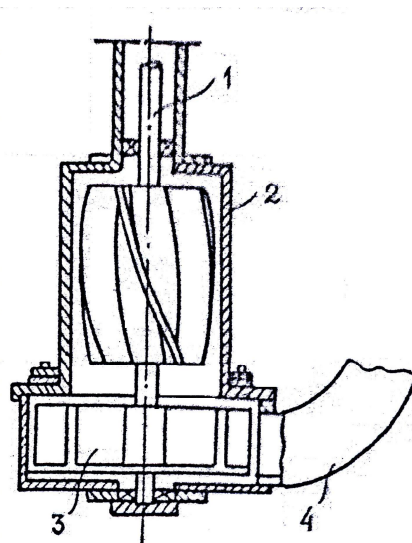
Схема насоса с измельчающим устройством в виде шнека (1 – вал 2 – корпус; 3 – рабочее колесо; 4 – всасывающая труба).
